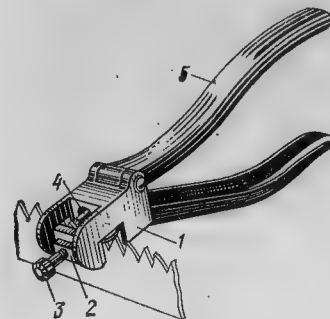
1 — корпус; 2 — матрица; 3 — винт регулировочный; 4 — пуансон; 5 — ручки
